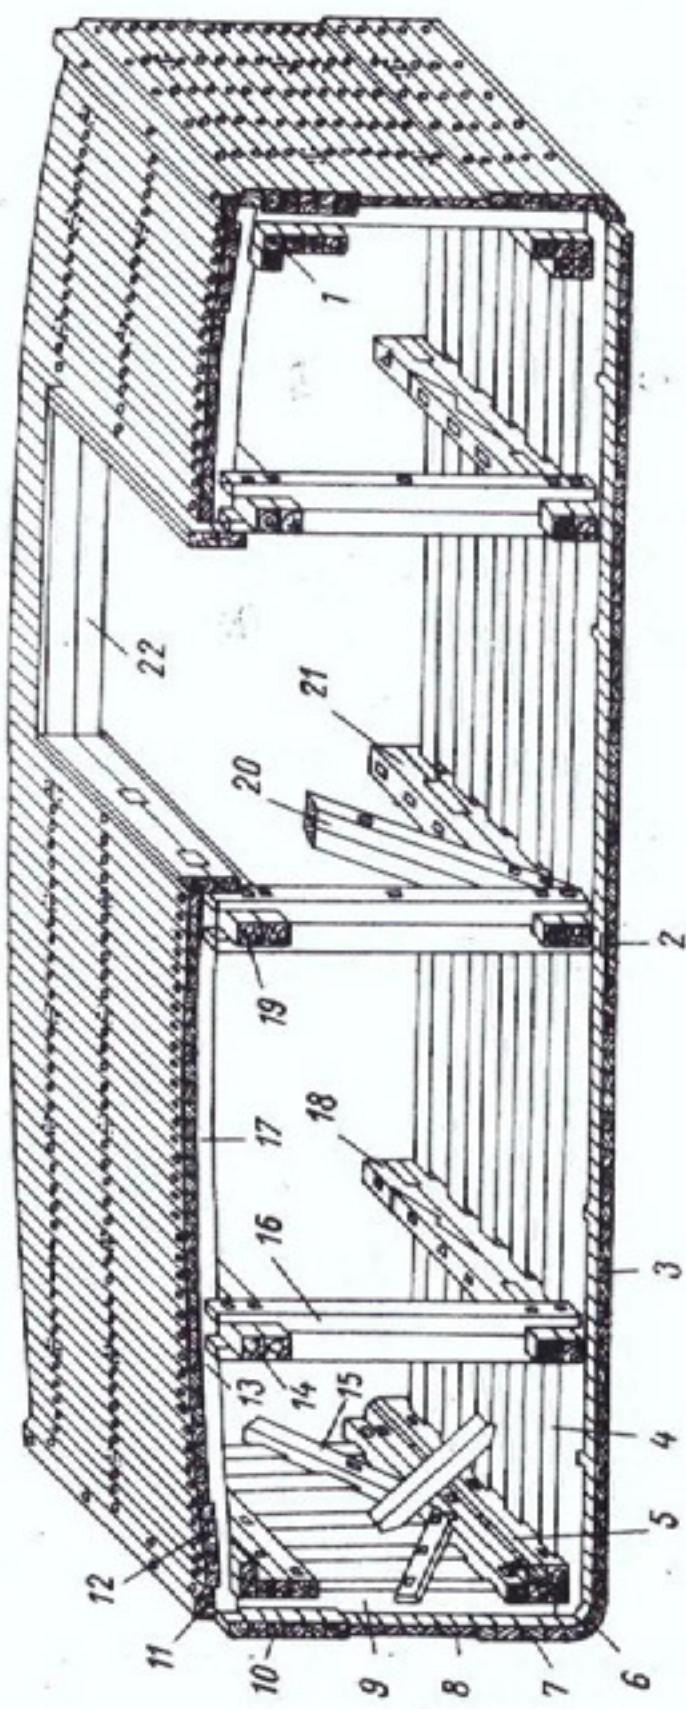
Схема расположения и наименования основных элементов корпуса речного судна баржевой конструкции.
